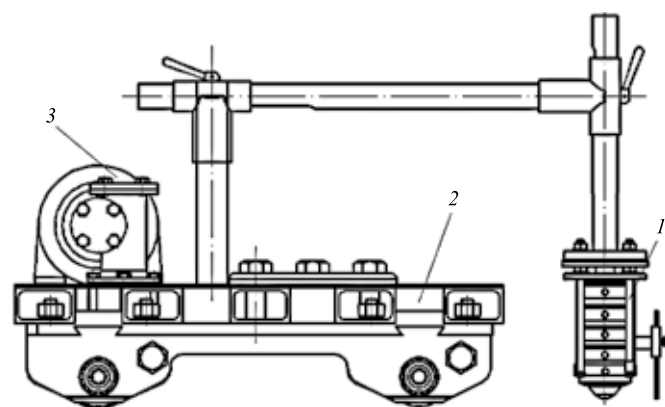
Переносное приспособление для упрочнения направляющих металлорежущих станков:
